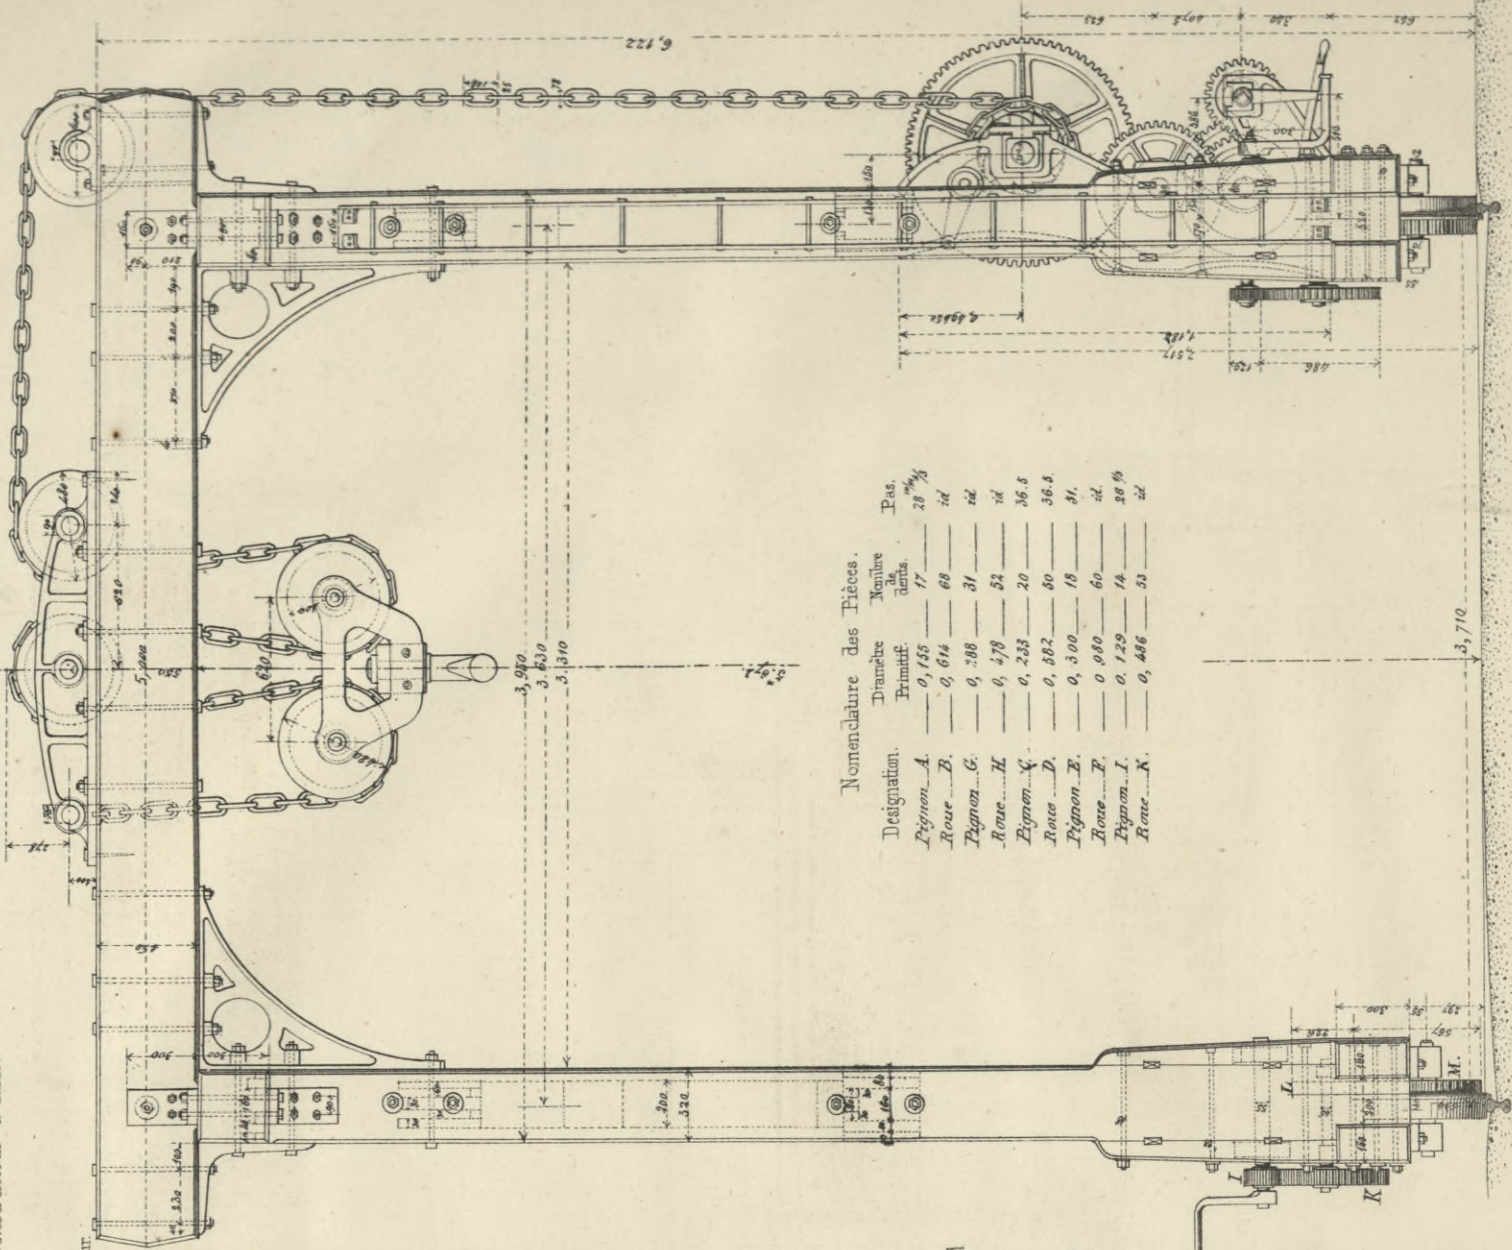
Vue perpendiculairement à la Voie à 0^m.03 pour 4^m.00.
